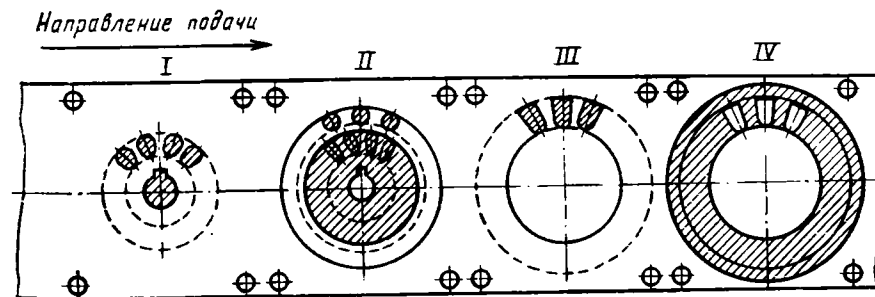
Четырехпозиционная схема штамповки листов статора и ротора
